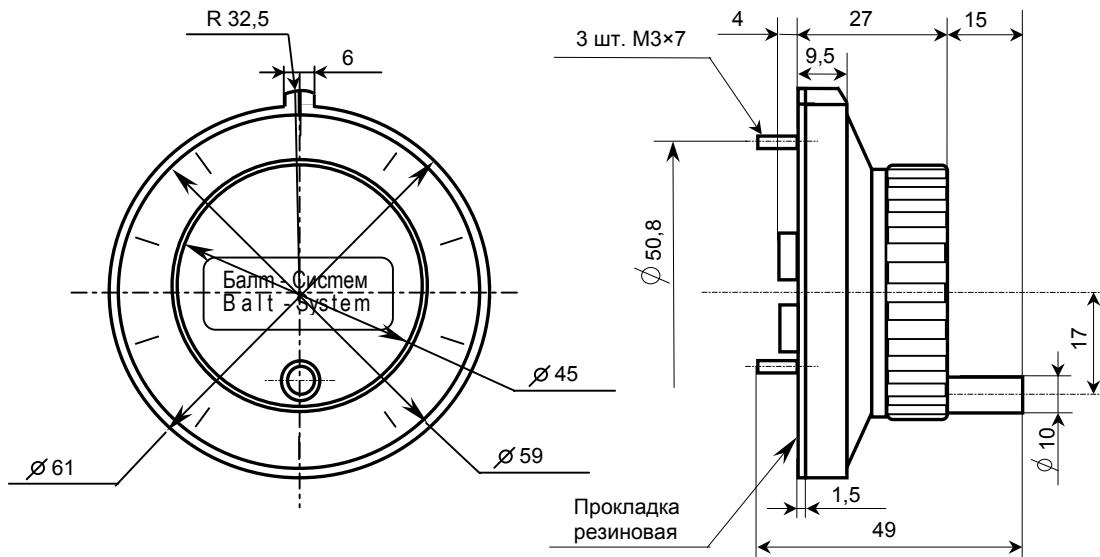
Габаритные размеры штурвала ZBG-5-003-100
